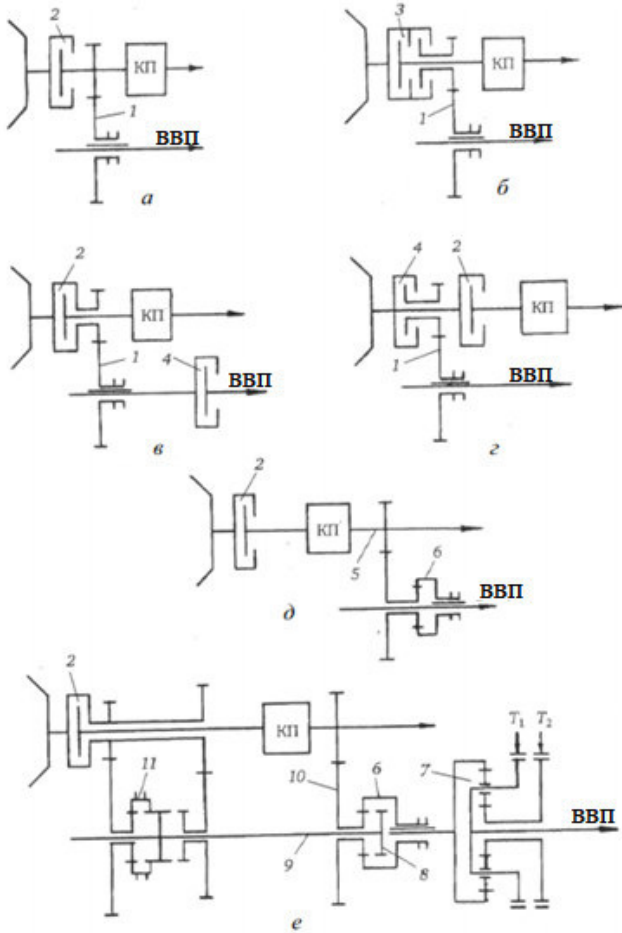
Схеми приводів валу відбору потужності: 1 – рухома каретка, 2 – головне зчеплення, 3 – подвійне зчеплення, 4 – зчеплення привода ВВП, 5 – вторинний вал коробки передач, 6 – зубчаста муфта, 7 – планетарний ряд, 8 – зубчастий вінець, 9 – вал, 10 – колесо з зубчастим вінцем, 11 – зубчаста муфта
